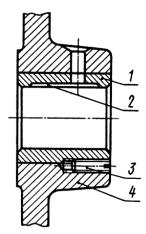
Неразъемный подшипник, встроенный в станину машины: *1* – втулка; *2* – смазочная канавка; *3* – стопорный винт; *4* – станина машины
